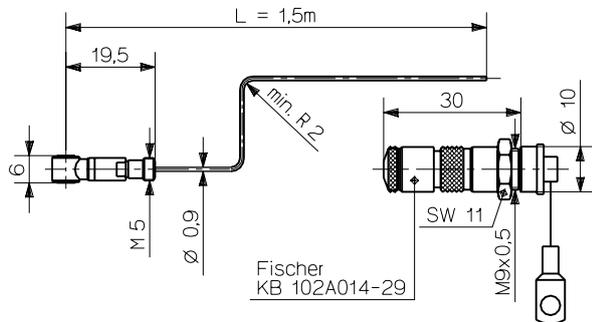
Kraftsensor Typ 9211BE mit Kabel und Stecker
